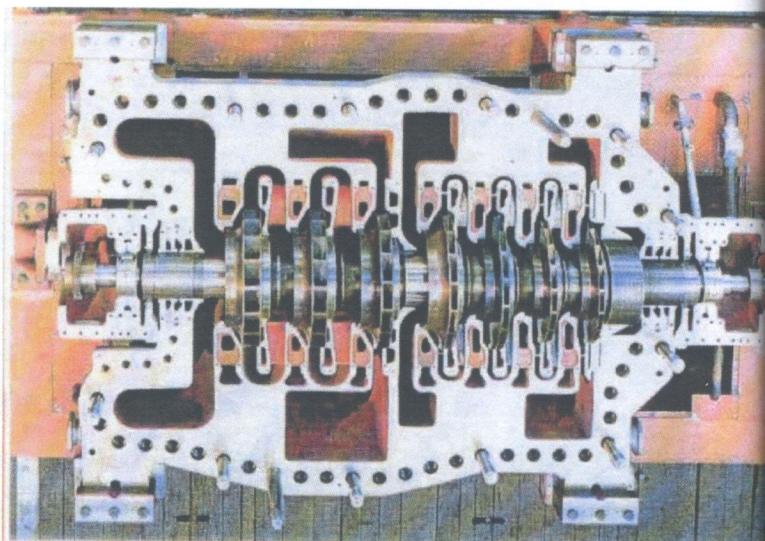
Загальний вигляд нижньої половини корпусу з ротором
